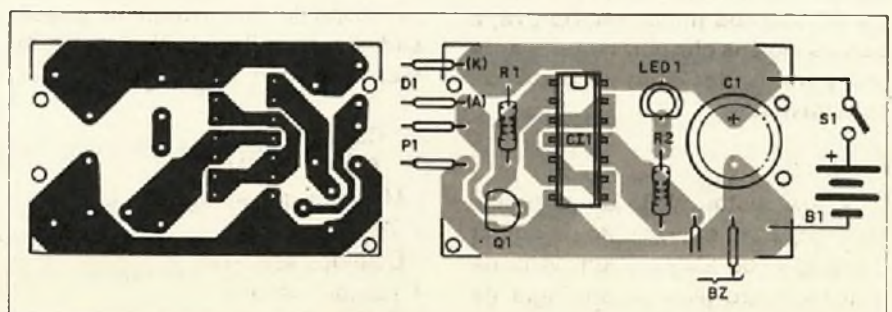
Placa de circuito impresso do teste de controles remotos.
